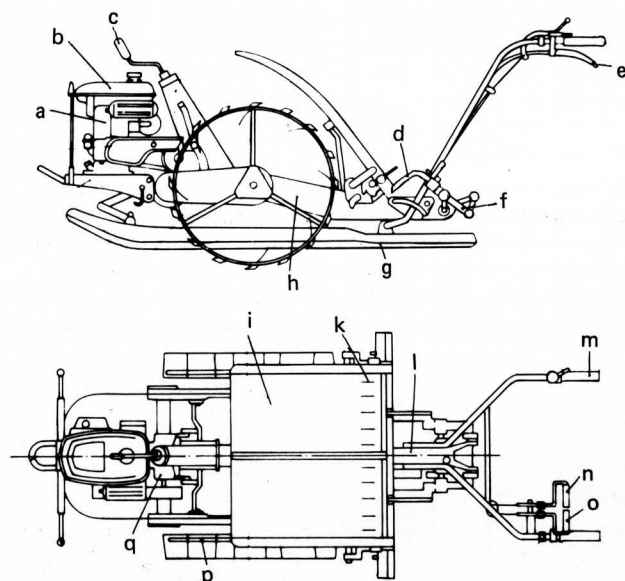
Aufbau einer Reispflanmaschine für Pflanzplatten.
